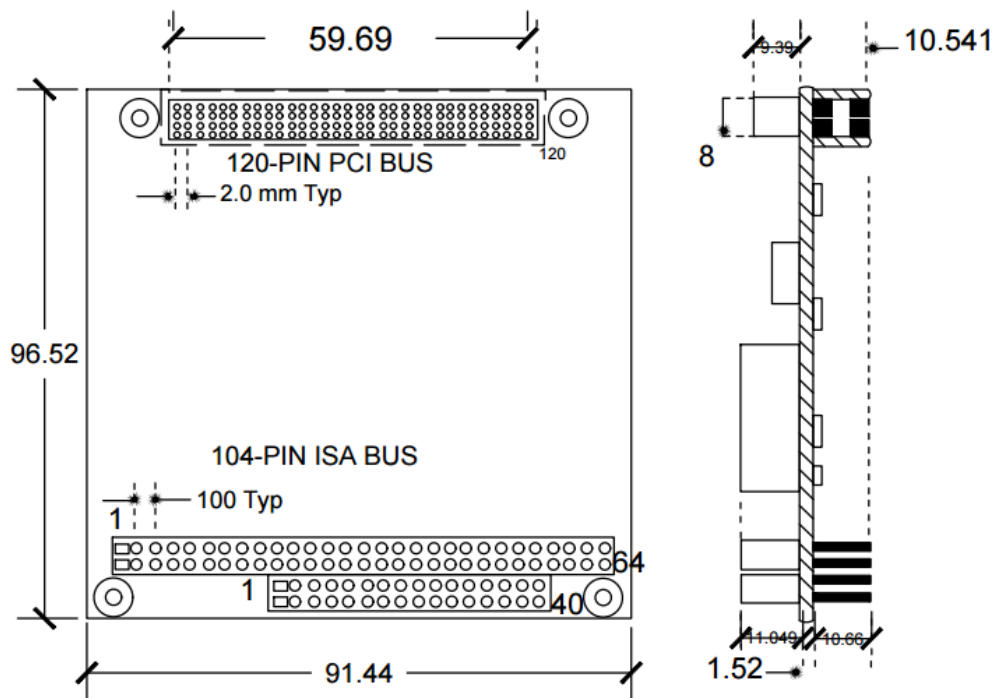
Estándar PC/104 Dimensiones de PCB.
